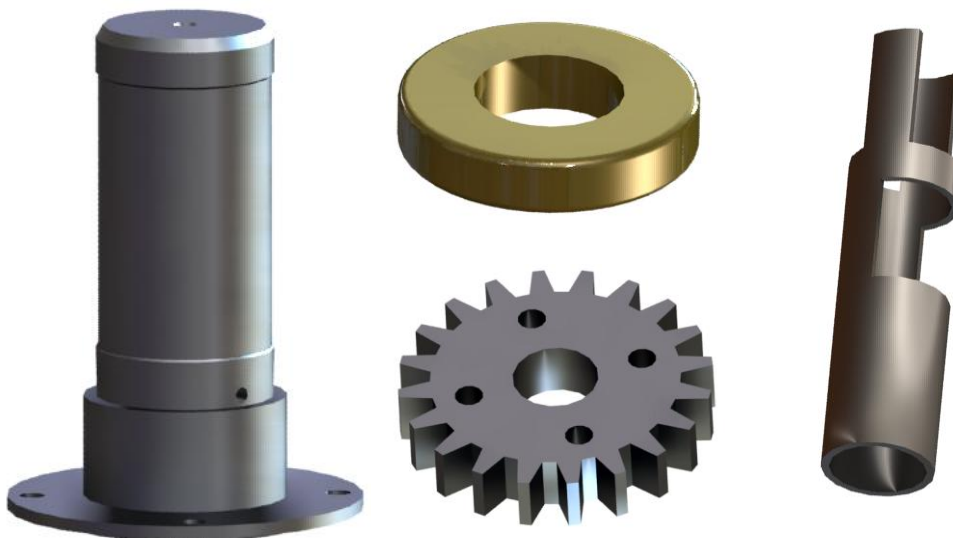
Bauteile des Helixturms, im CAD gezeichnet (links der Zentralzylinder, rechts ein Hubarmträger)
